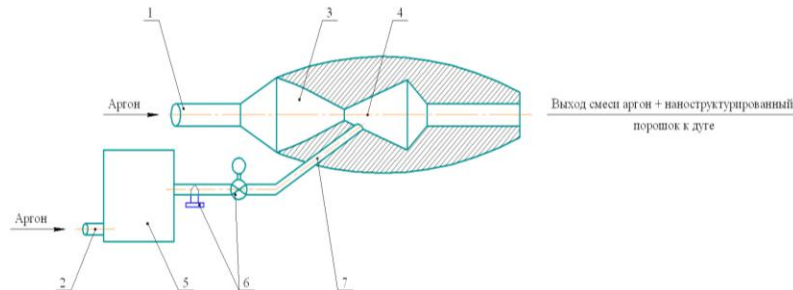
Схема устройства подачи нанопорошка в зону сварки:
